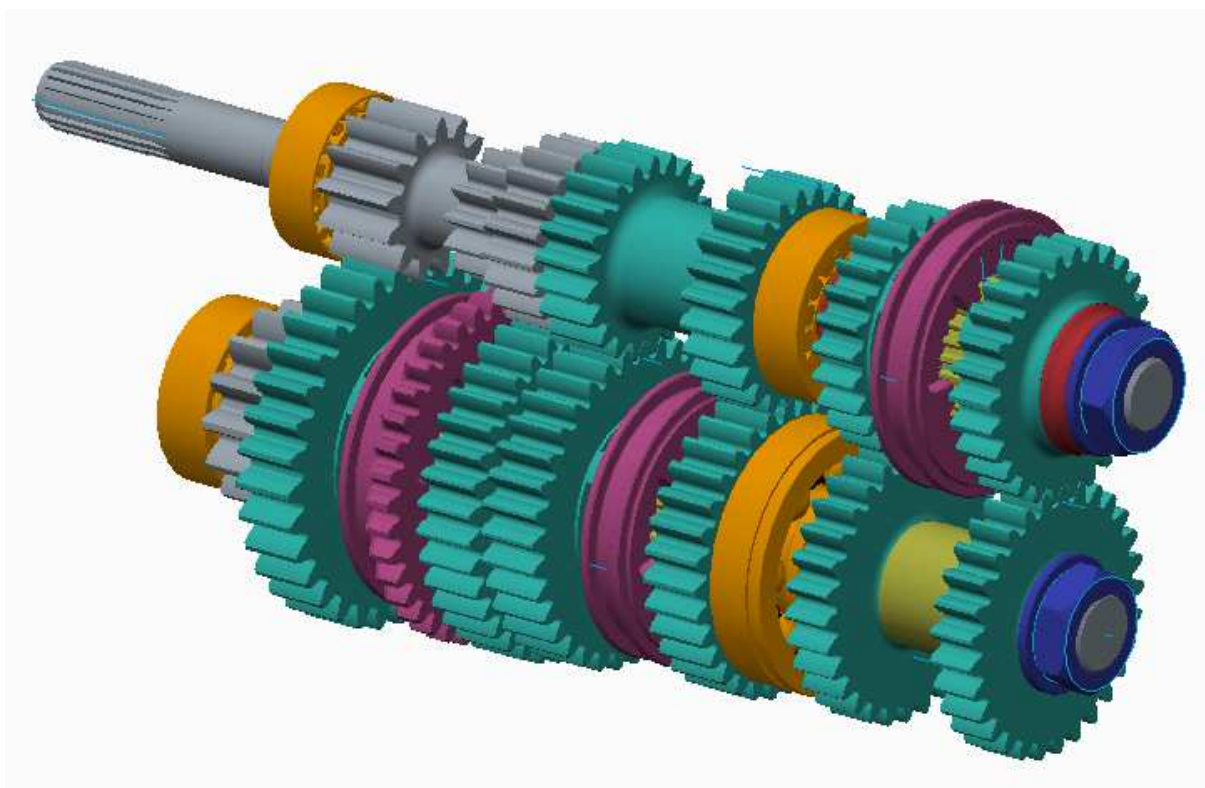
Upravená část řadicího ústrojí (pohled 3)
